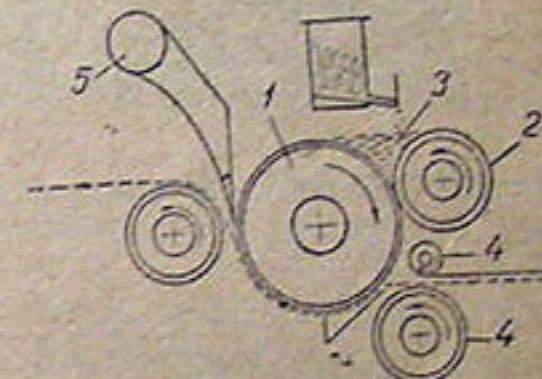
Схема машины для намазки обложки: 1 — цилиндр для намазки; 2 — цилиндр для растирания крахмала; 3 — крахмал; 4 — направляющий цилиндр; 5 — съемочная цапка.
